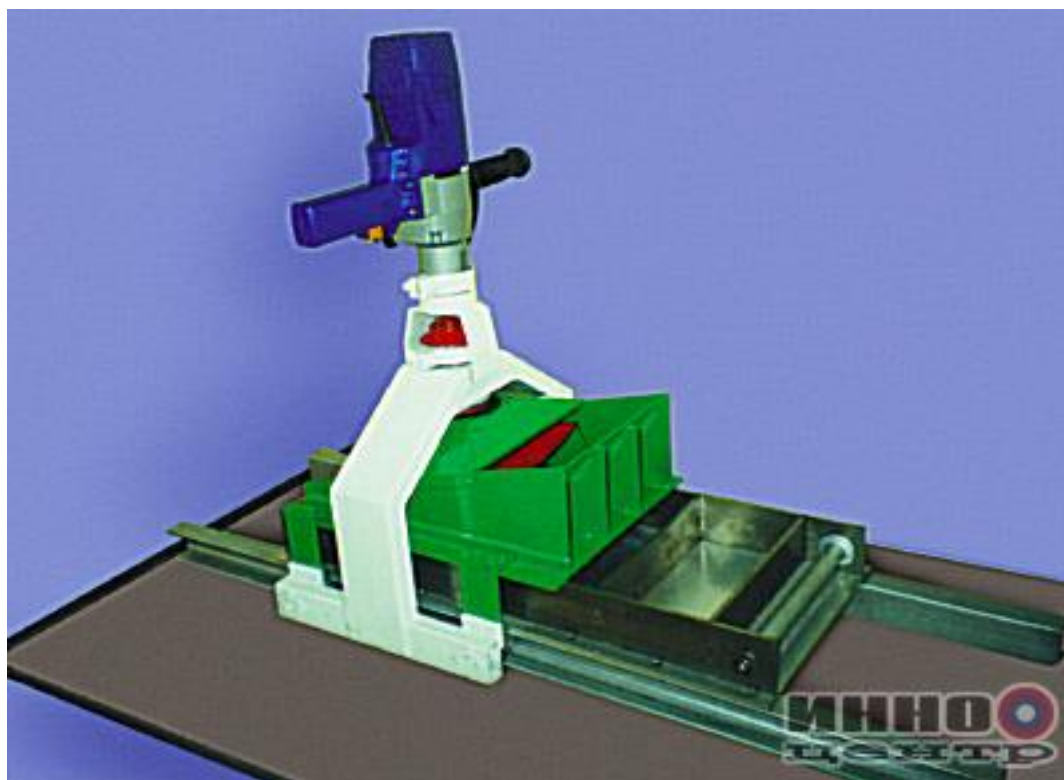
Формовочная насадка на механизированный инструмент МН05
